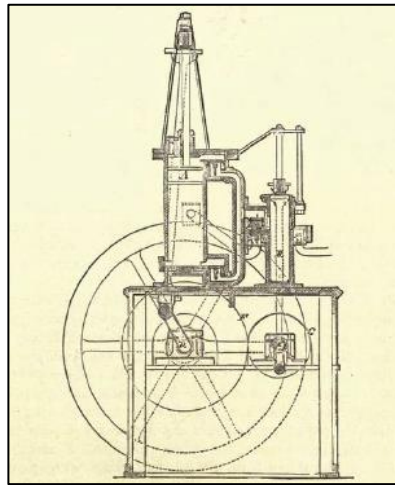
Motor de William Barnett (Espinosa, 2019)
